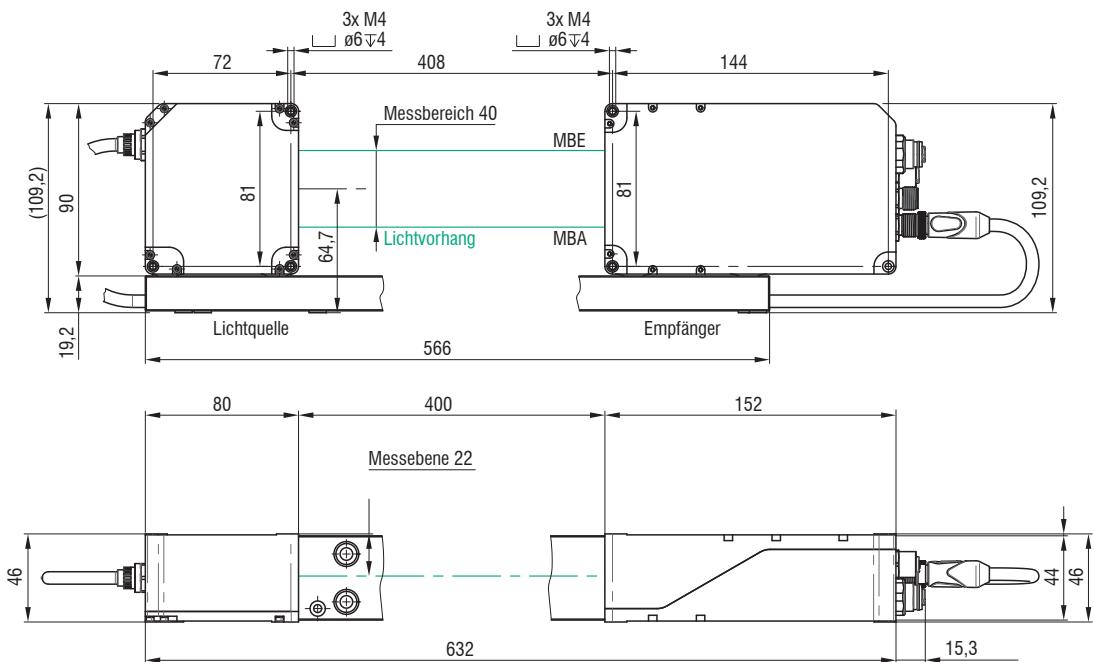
Maßzeichnung Lichtquelle und Empfänger ODC2700-40(002), Abmessungen in mm
